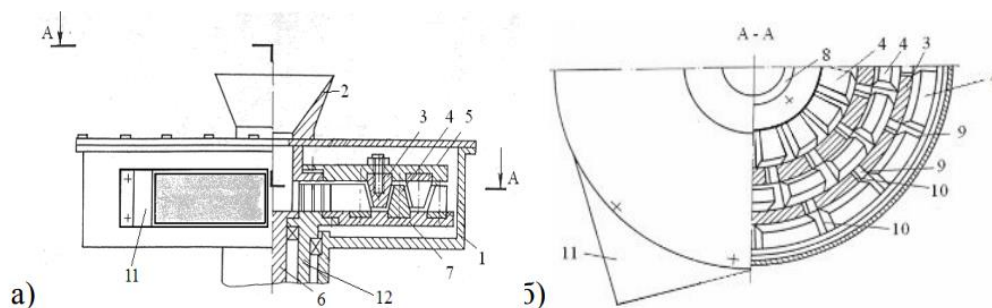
Схема центробежно-роторного измельчителя (а) и его режущих поверхностей (б): 1 – корпус; 2 – патрубок загрузочный; 3, 4 – режущие элементы; 5 – диск-ротор верхний; 6 – вал внутренний; 7 – диск-ротор нижний; 8 – окна радиальные; 9 – каналы (пазы); 10 – стенка канала; 11 – патрубок выгрузной; 12 – вал.
